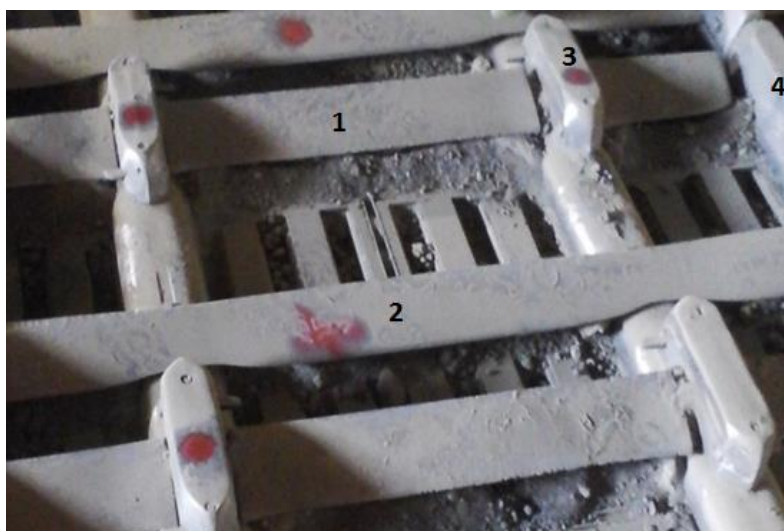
Abraçadeiras e barras marcadas para substituição
